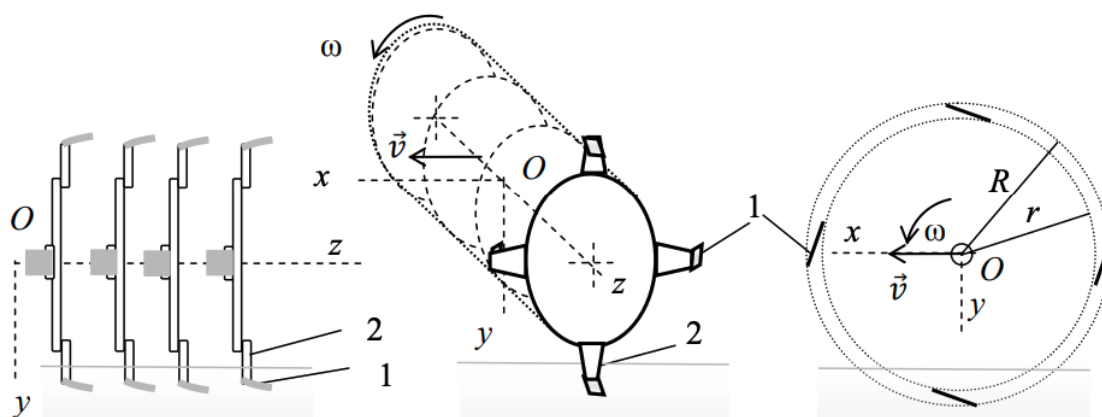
Барабан фрезы с ножами 1 и боковинами с режущими кромками 2
